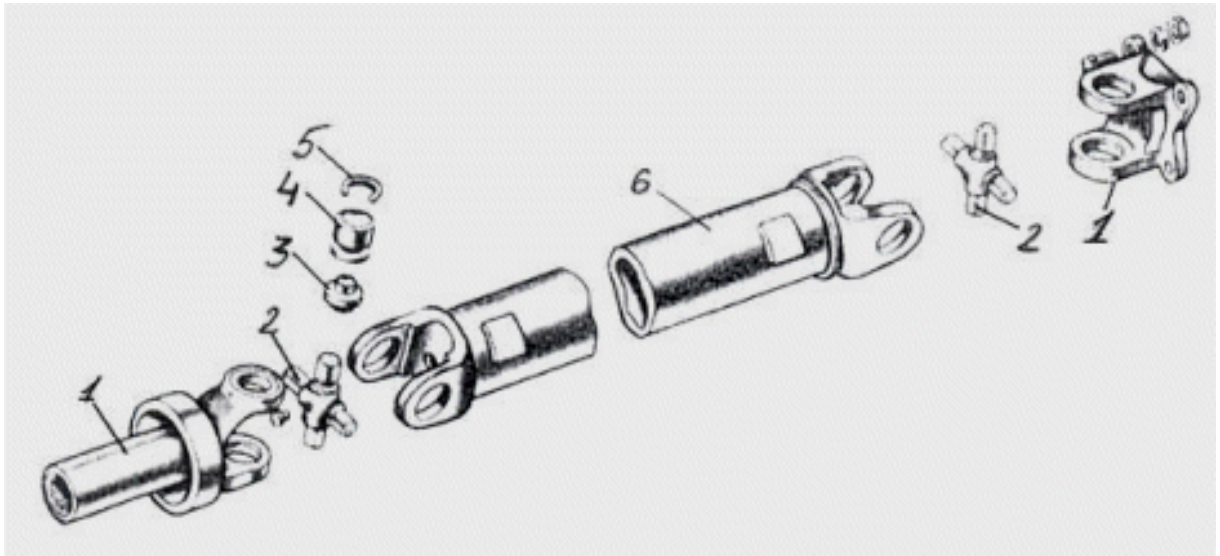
Карданный вал: 1,7 – скользящая и фланцевая вилки, 2 – крестовина, 3 – сальник, 4 – игольчатый подшипник, 5 – стопорное кольцо, 6 – труба вала.
